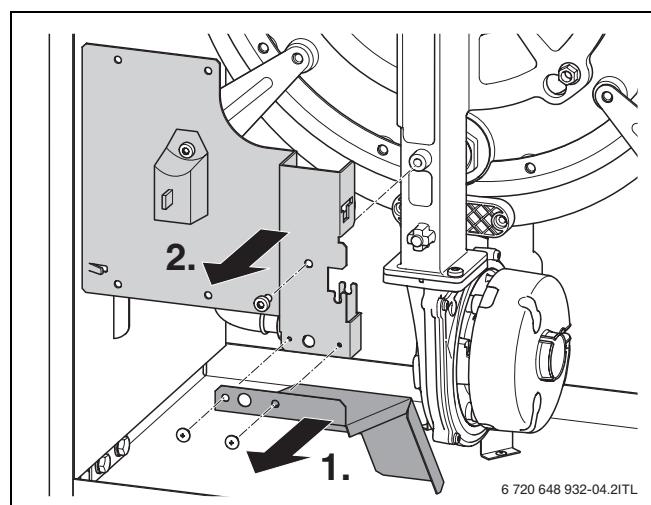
Smontaggio di lamiera di protezione dallo sgocciolamento lamiera di bloccaggio
